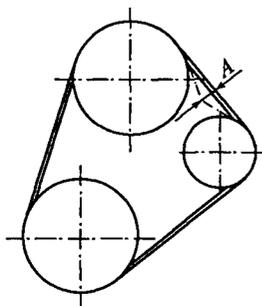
Схема проверки натяжения ремня привода насоса охлаждающей жидкости двигателей моделей 331, 3317, 3313
